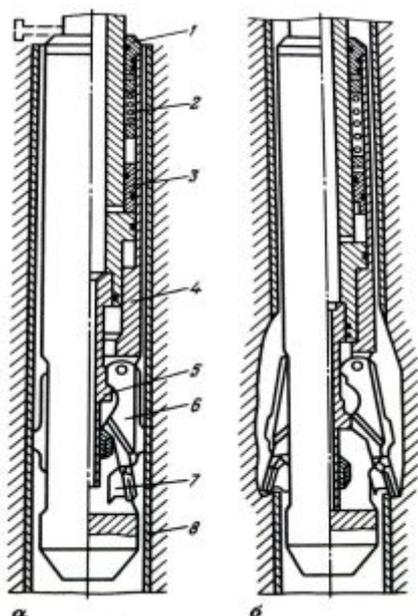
Схема фрезера Каммерера в транспортном (а) и рабочем (б) положениях [6]:
